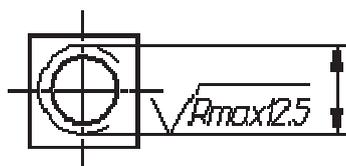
Пример обозначения шероховатости внутренней резьбы
